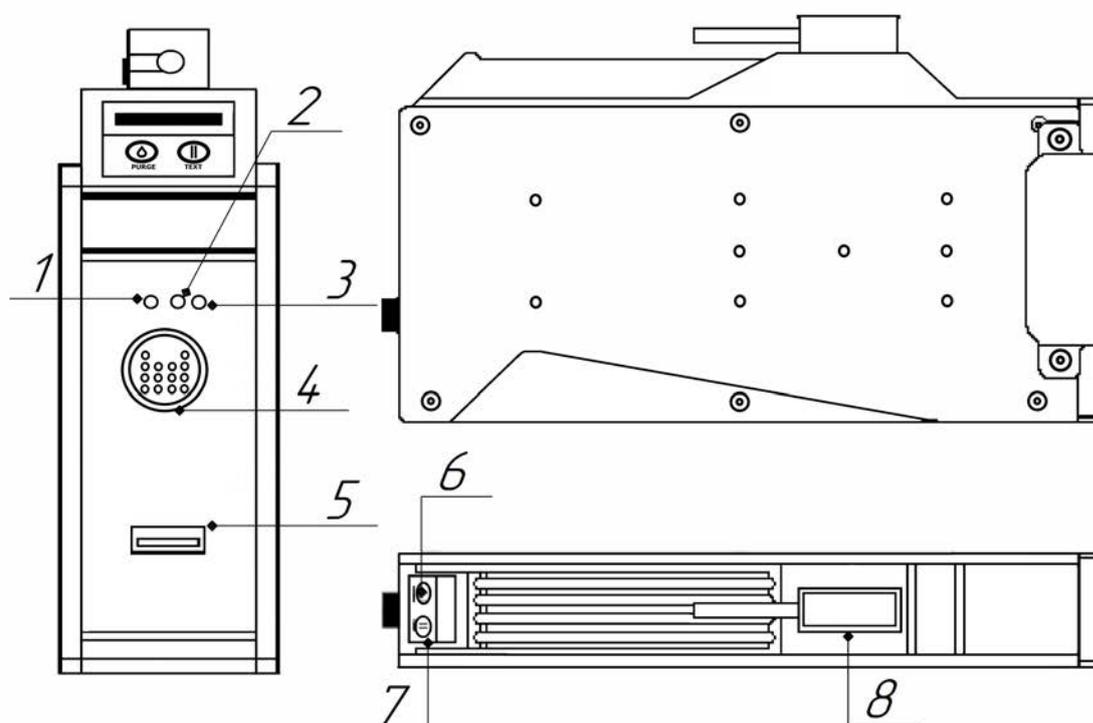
Внешний вид боковых поверхностей печатающей головки типа 8D. Условные обозначения: см рисунок 4.
